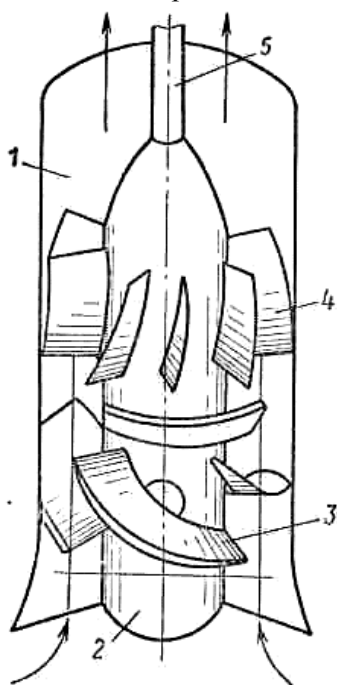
Схема осьового нагнітача: 1 – корпус; 2 – втулка; 3 – робочі лопаті; 4 – напрямні лопаті; 5 – вал
